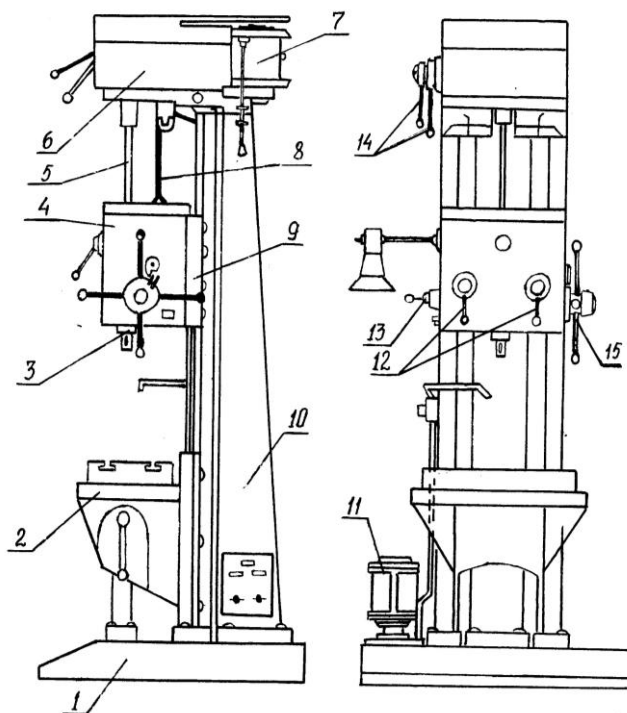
Общий вид вертикально-сверлильного станка 2A125.
